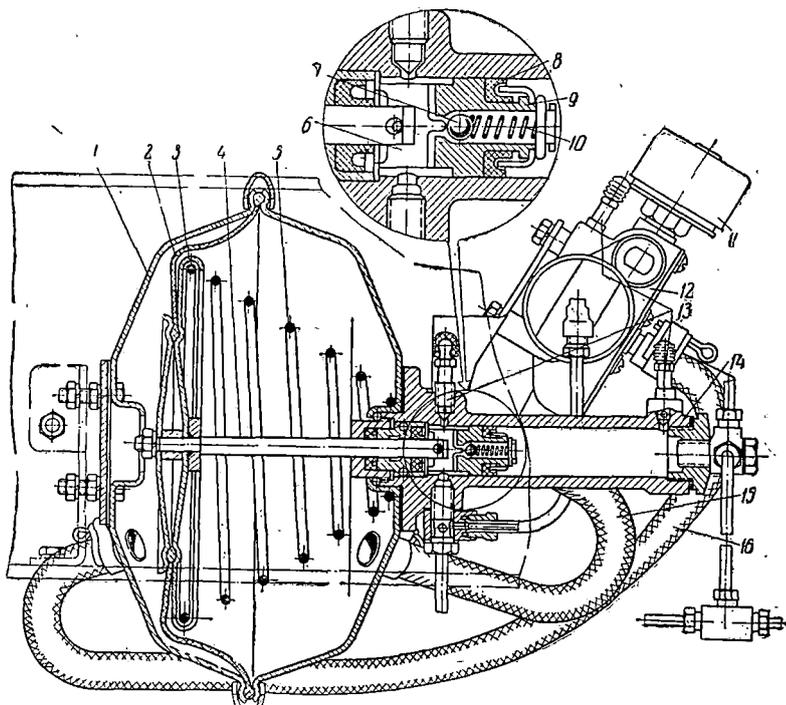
Схема гидровакуумного усилителя тормозов автомобилей ГАЗ-53 и ГАЗ-66:
